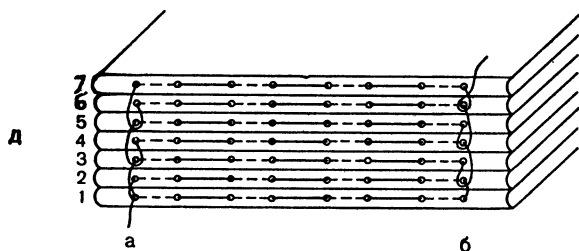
Шитье книжного блока и другие виды скрепления листов:
